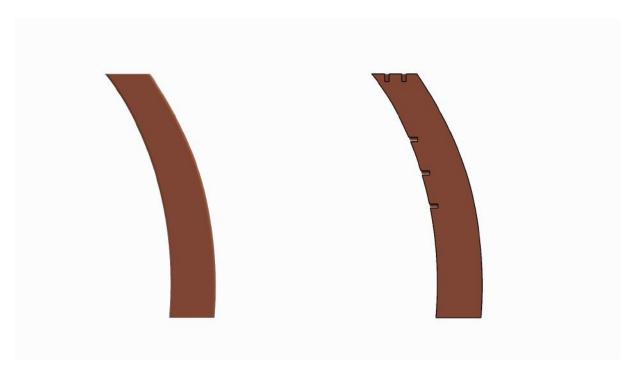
Detalhe em corte Pés Frontais - Furos para cavilhas
